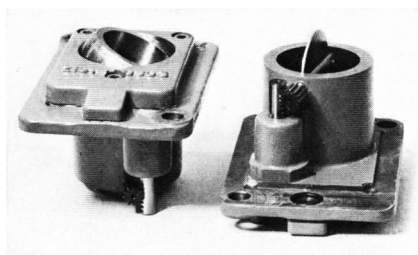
Luftkontrollgehäuse zum Fertigformenhalter. Deutlich sichtbar die Luftklappe mit ihrer Betätigung.
